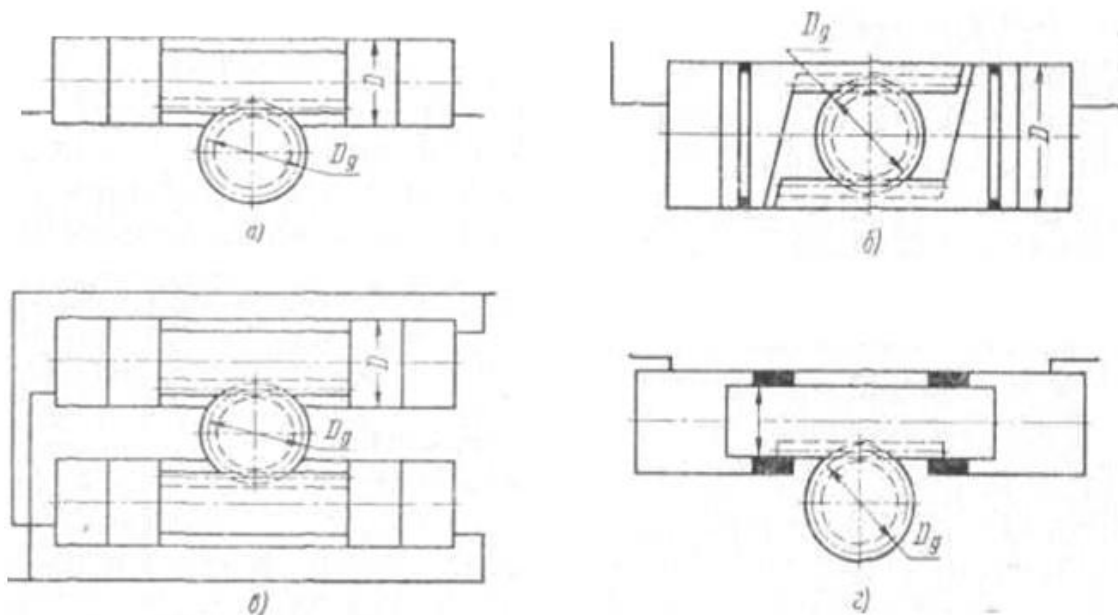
Схемы поворотных гидроцилиндров с реечной передачей
